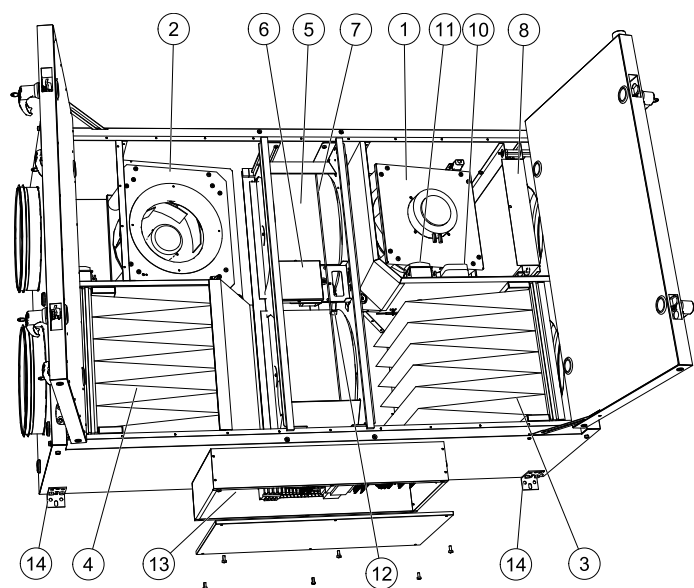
Componenti delle unità HW (in caso di batteria di riscaldamento ad acqua installata)
